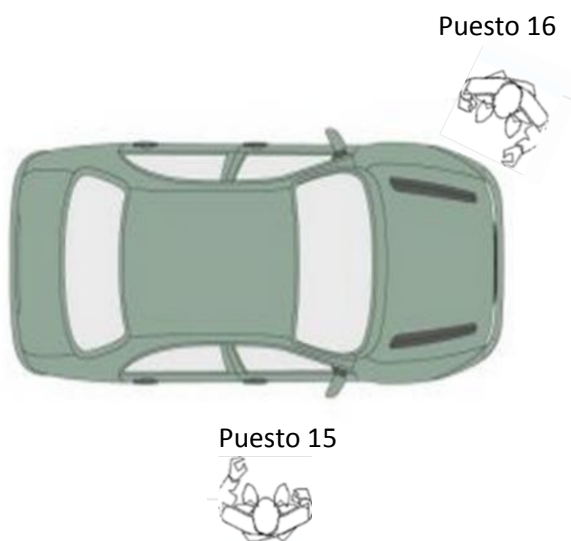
Puestos de estación n° 5. Fuente: Elaboración propia.
